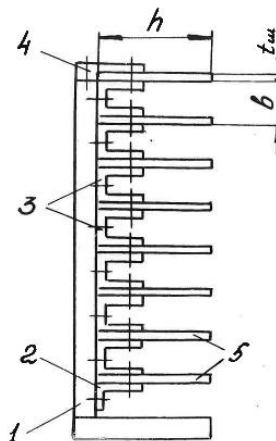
Приспособление для обработки шаблонов конических деталей на карусельном станке: 1- плита; 2, 4 – нижняя и верхняя накладки; 3 – упоры; 5 – заготовки сменных шаблонов.
